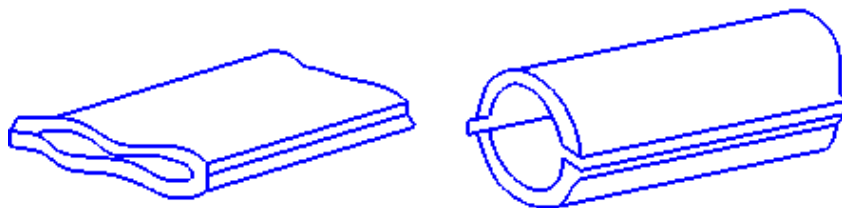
Схема при получении трубы из упаковки пакетного типа с использованием двух заготовок: а) трубный пакет; б) труба, полученная после нагревания пакета
